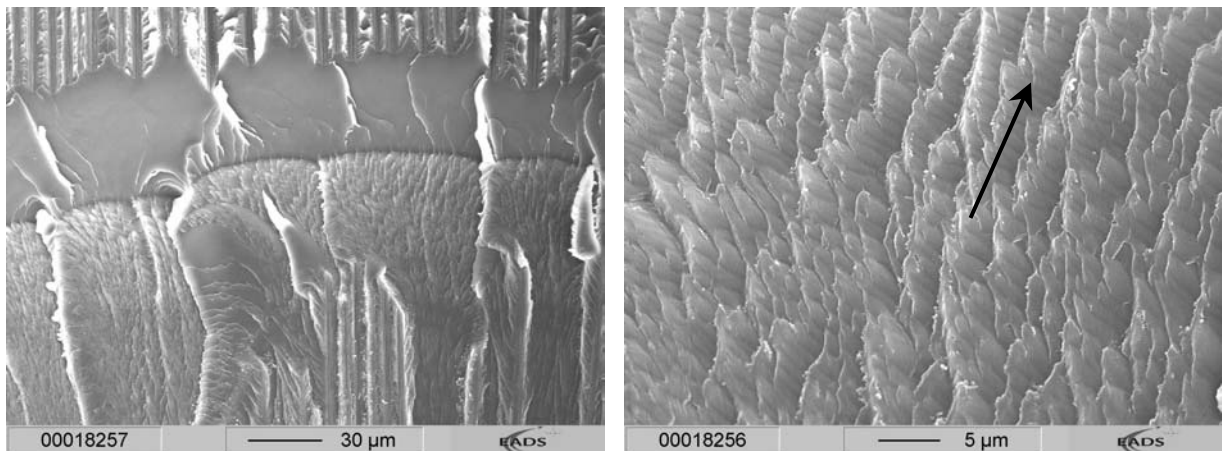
Bereich B – schuppige Strukturen am Ende des Ermüdungsbereiches mit eingezeichneter Bruchrichtung
